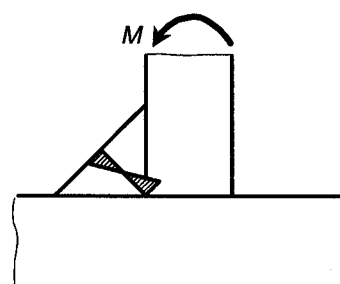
Tensiones en la raíz de una soldadura en ángulo
